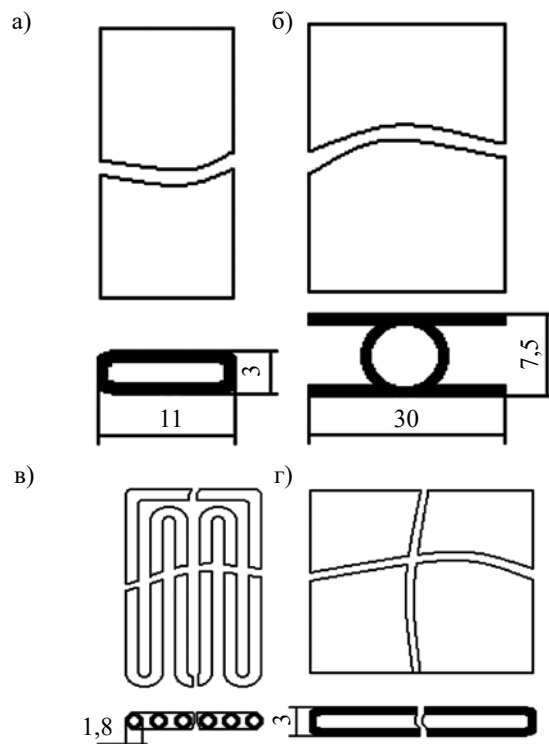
Форма корпусу двофазних теплопередавальних пристроїв:
